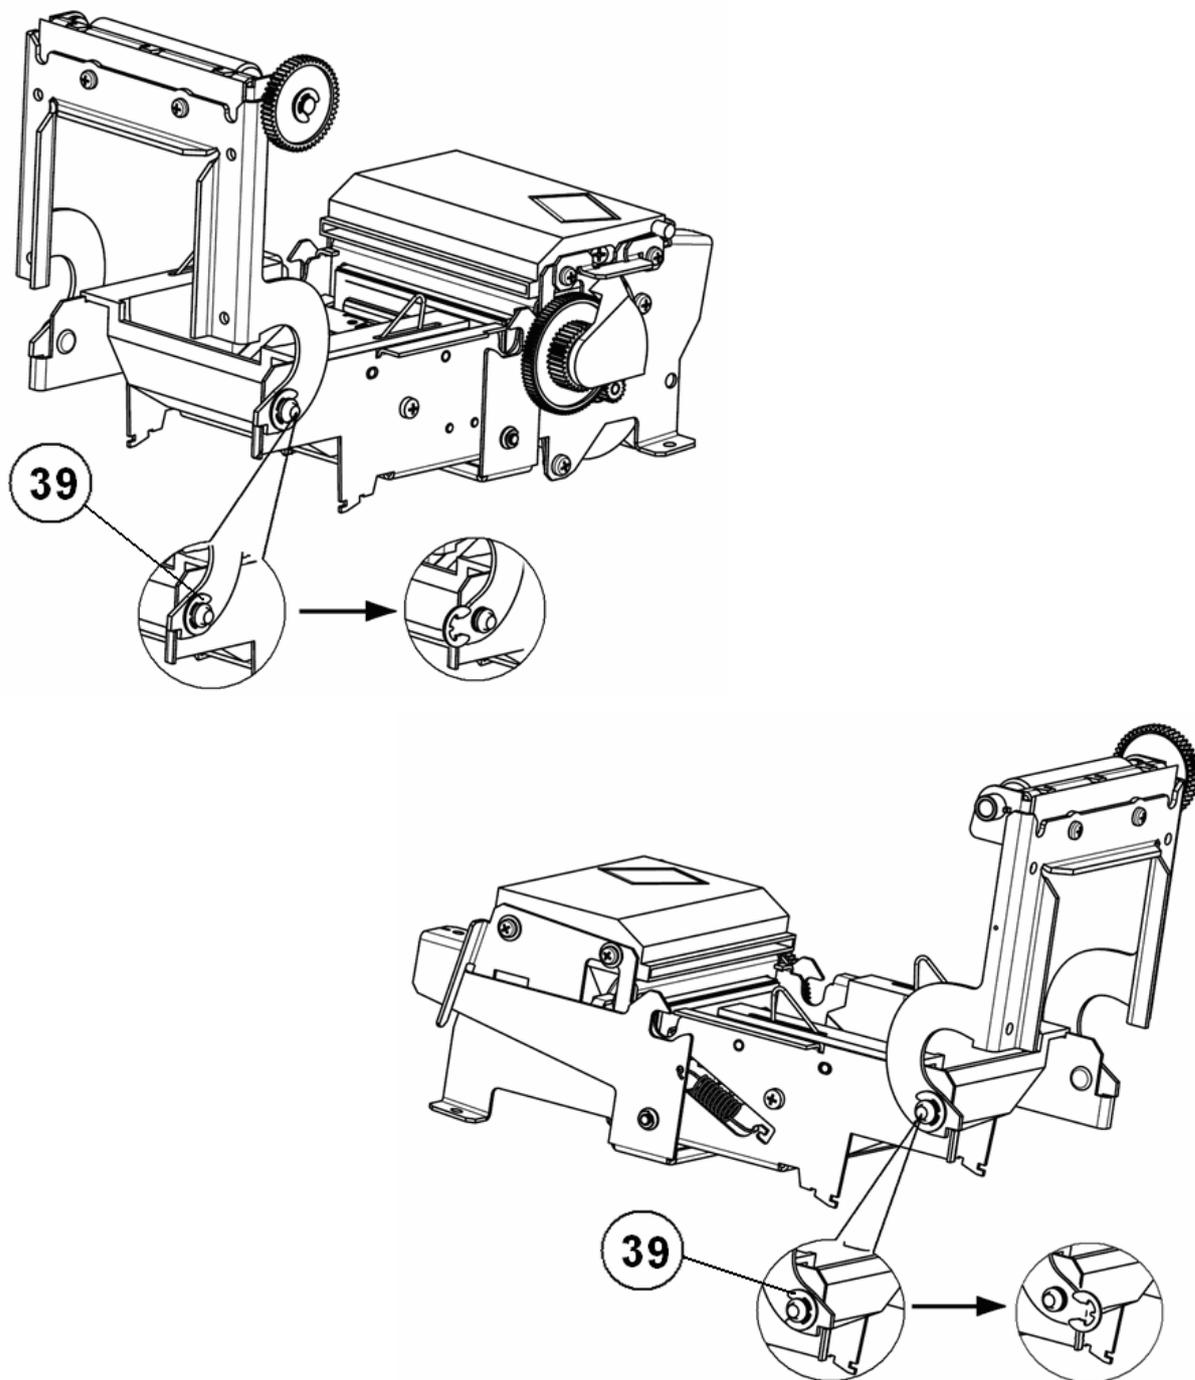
Стопорные шайбы крепления шасси крышки.
